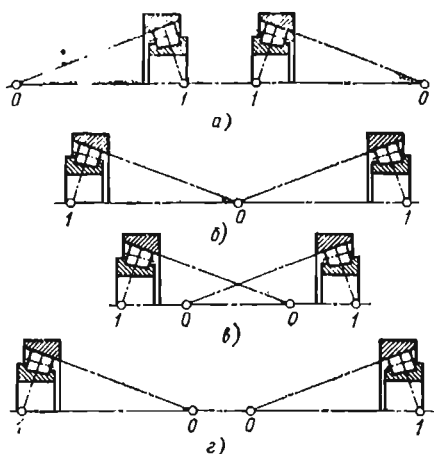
Схемы установки подшипников в регулируемых опорах вала:
